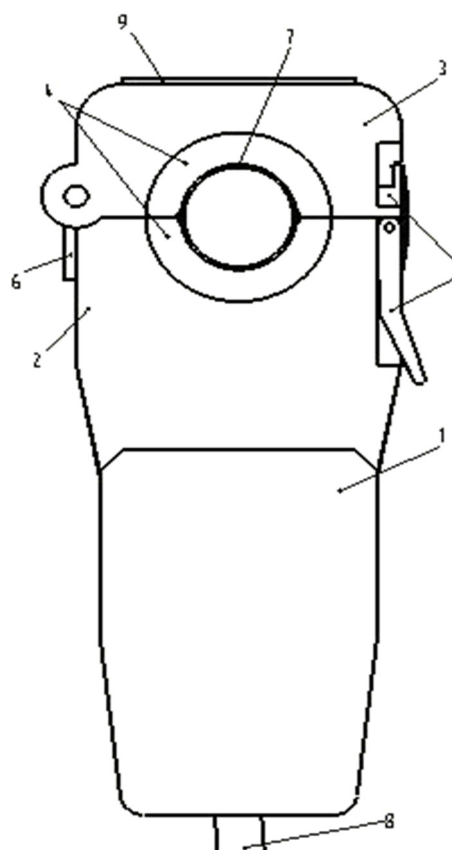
Общий вид: 1 – корпус головки; 2 – нижняя облицовочная пластина; 3 – верхняя облицовочная пластина; 4 – фиксатор; 5 – замок; 6 – блок поворотного крепления; 7 – изделие (труба); 8 – шланг подачи; 9 – верхняя пластина со смотровым стеклом.
